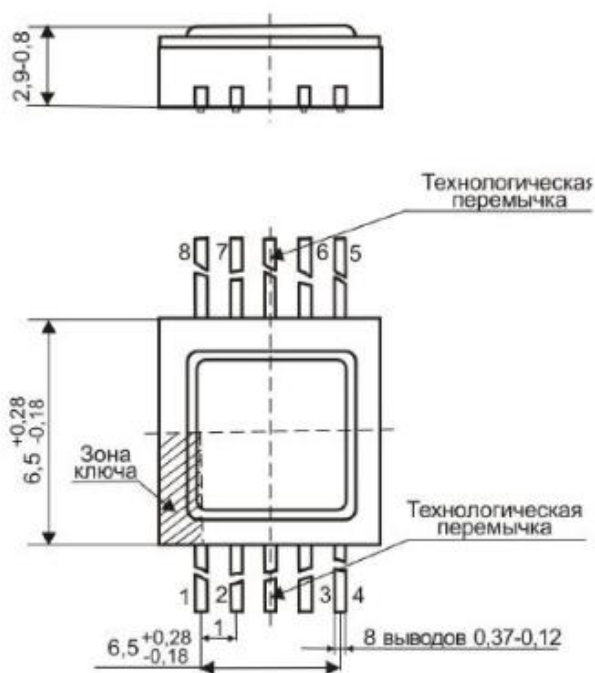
размер корпуса микросхемы 142EP2УИМ
